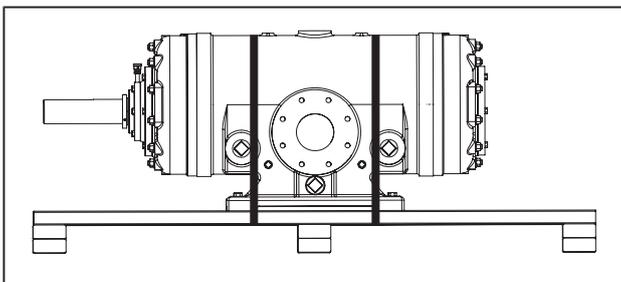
Закрепление компрессора при транспортировке. Запрещается привязывать компрессор за крышки цилиндра или вал ротора.
